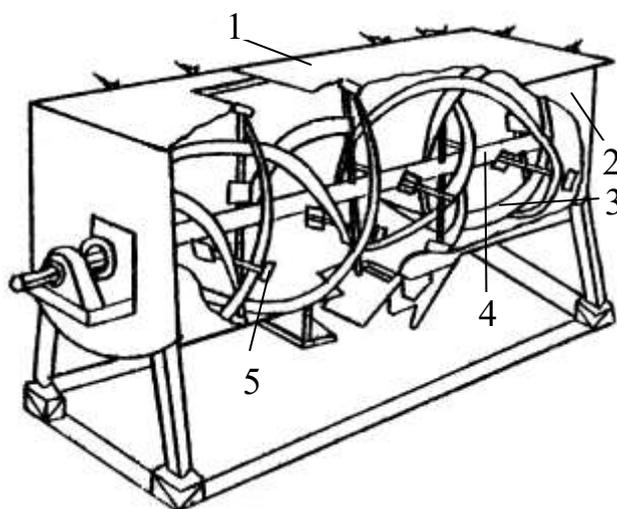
Горизонтальный смеситель с комбинированными рабочими органами:
